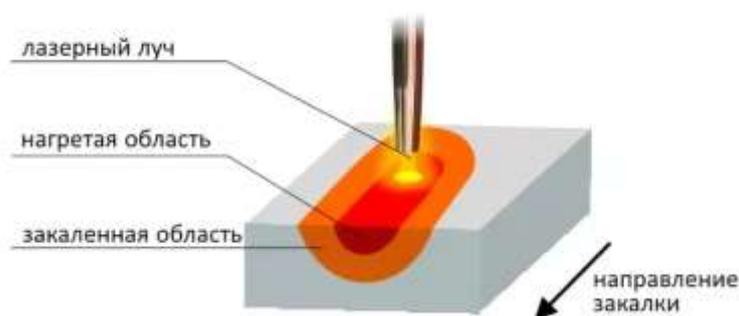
Схема нагрева обрабатываемой поверхности изделия.
